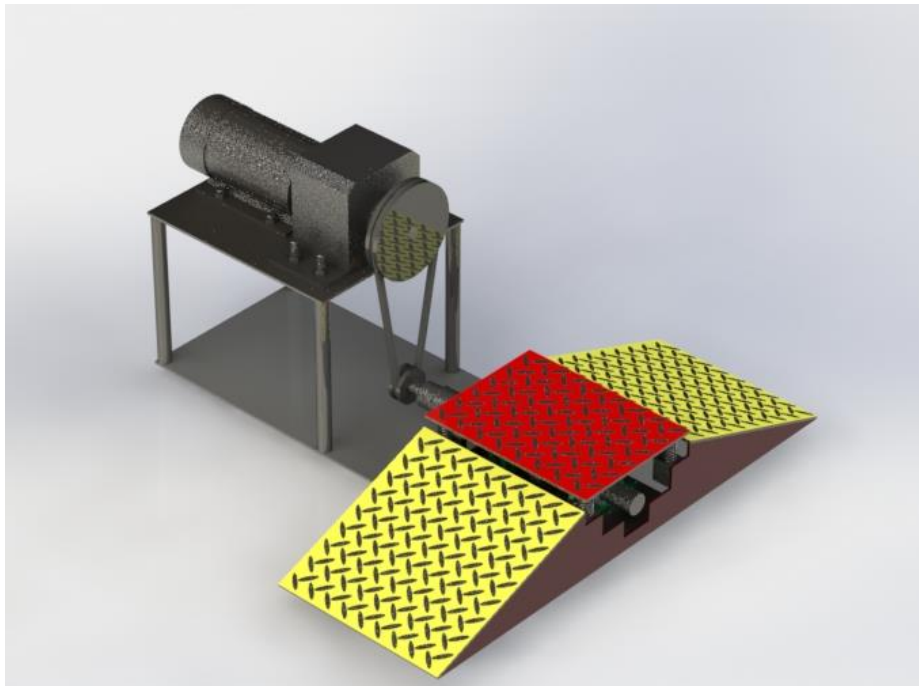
Modelo del banco de pruebas a construir, renderizado en SolidWorks.
